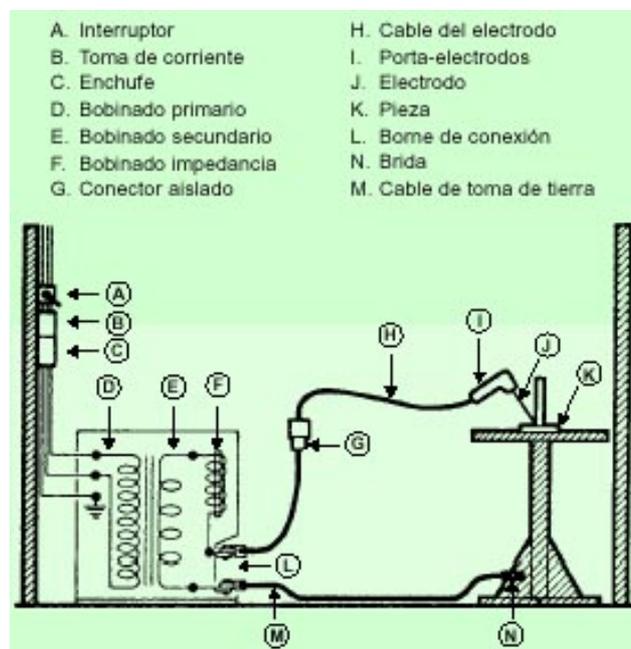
Instalación segura de un puesto de soldadura CA con transformador.
